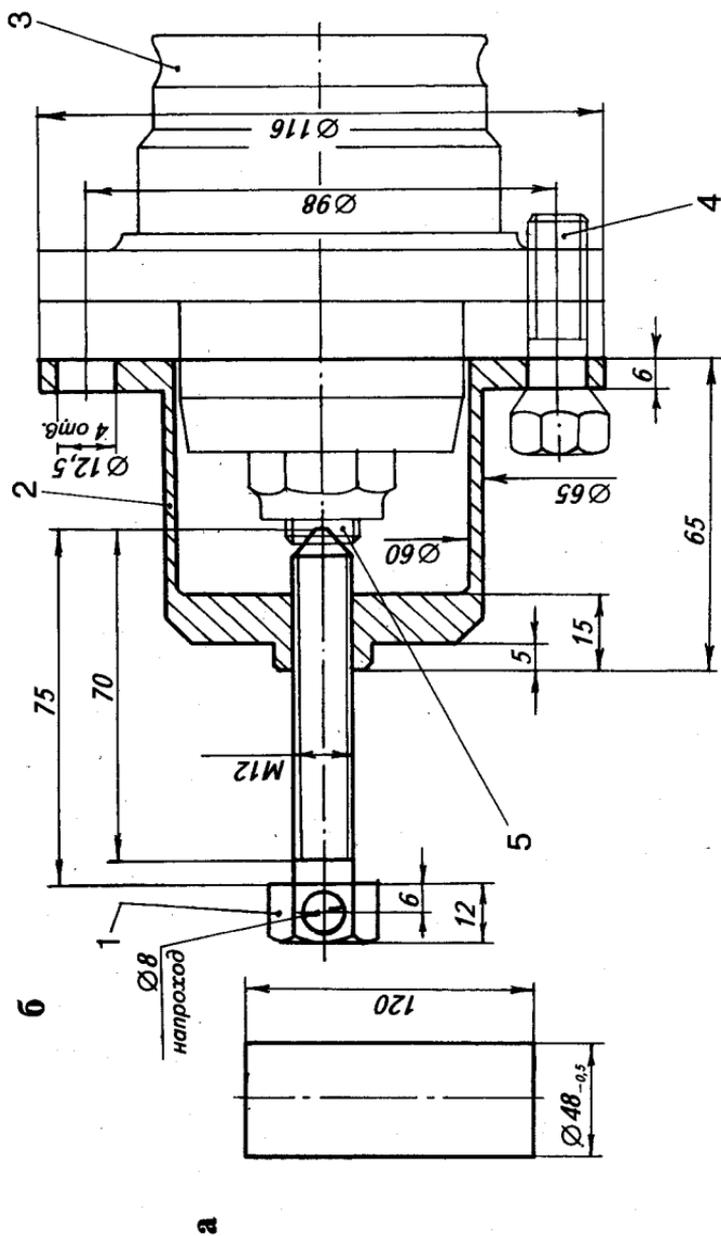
Съемник для выпрессовывания ступицы переднего колеса и сальника: а — оправка для выпрессовывания сальника (материал: дерево, алюминиевый сплав); б — выпрессовывание ступицы; 1 — винт; 2 — стакан; 3 — ступица; 4 — штатный болт крепления колеса; 5 — поворотная цапфа (куллак).
